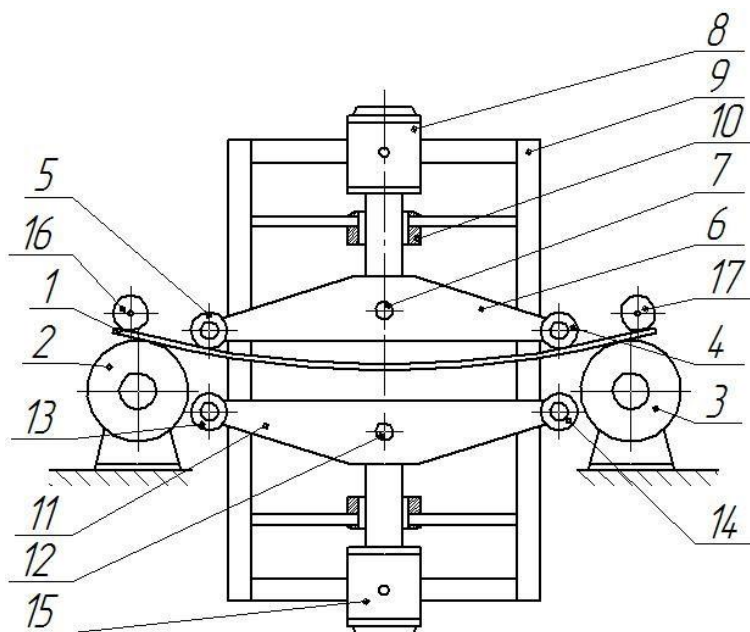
Схема для изгиба заготовки в двух противоположных направлениях
